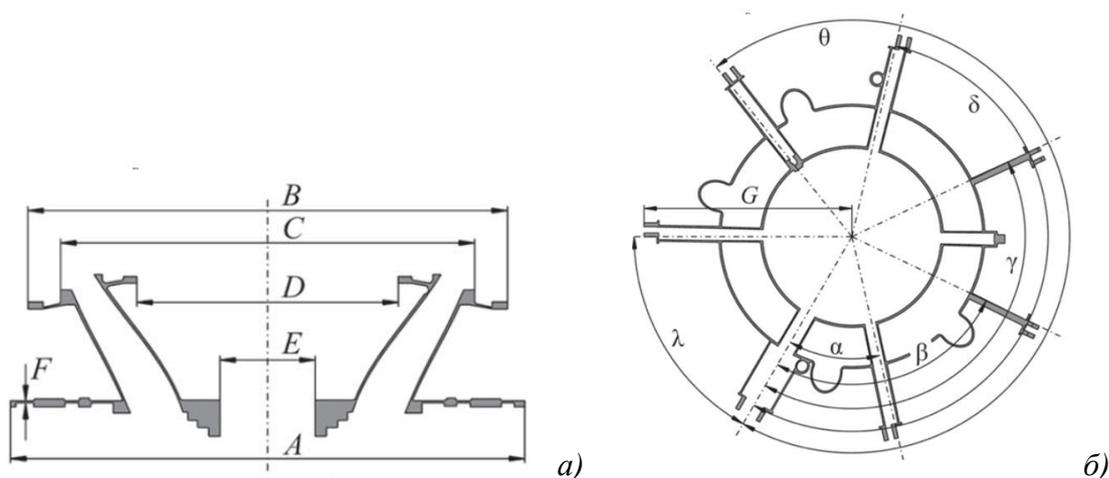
Сечения модели отливки «Втулка» с размерами, которые измеряли в отливке а) вертикальное б) горизонтальное
